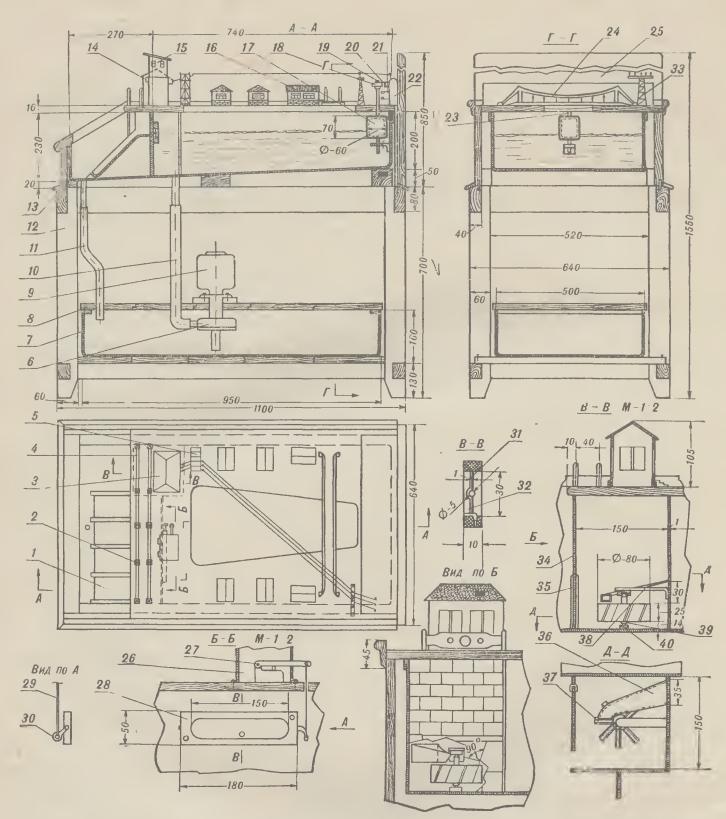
Модель ГЭС с автоматическим упривлением (схема и детали):
